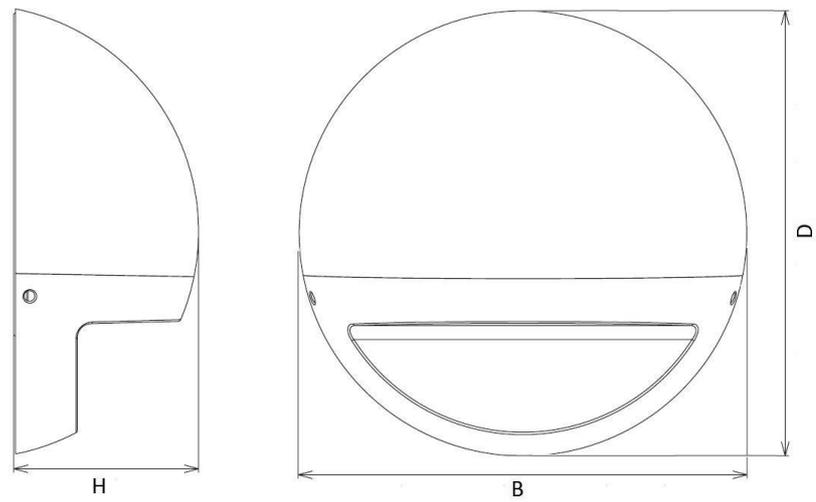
Общий вид, габаритные размеры светильника ДБО06.
